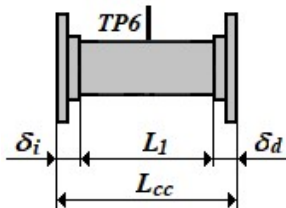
Prototipo TC-01-(0.4/2). Dimensiones de la cámara de compresión.
